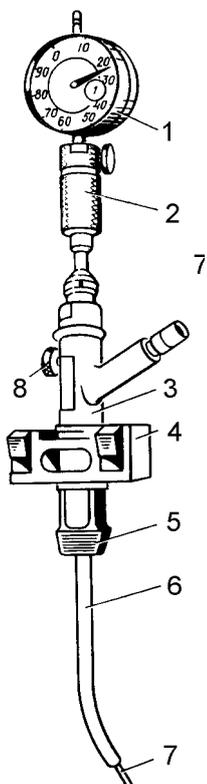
Прибор КИ-11140 для измерения зазоров в кривошипно-шатунном механизме
